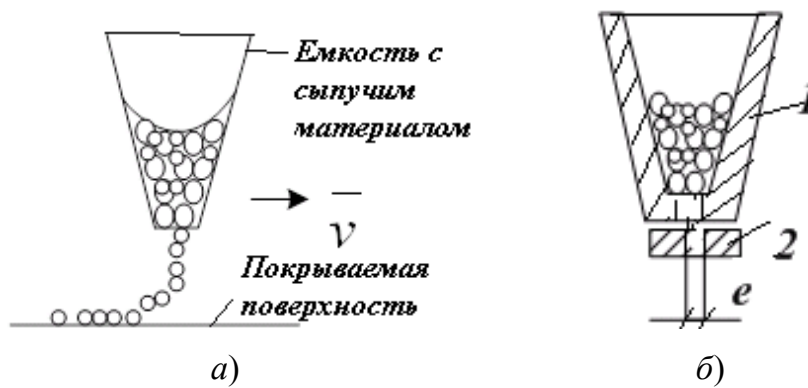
Схемы устройства подачи сыпучего материала на поверхность:
